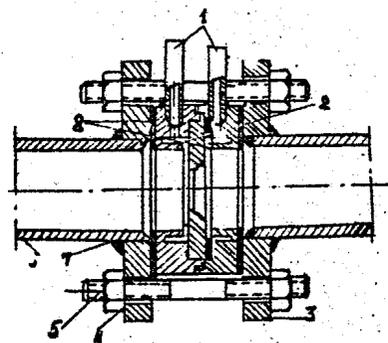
Камерная диафрагма: 1 - отборные трубки; 2 - кольцевые камеры; 3 - фланец; 4 - гайка; 5 - шпилька; 6 - трубопровод; 7 - диск диафрагмы; 8 - прокладки.
